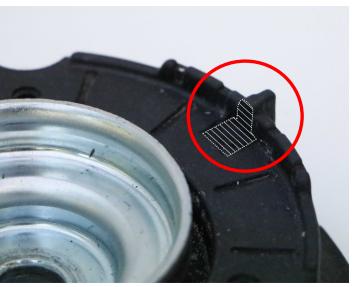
Verdrehsicherung des Stützlagers entfernen *Fig 1:* Remove the rotation lock of support bearing
